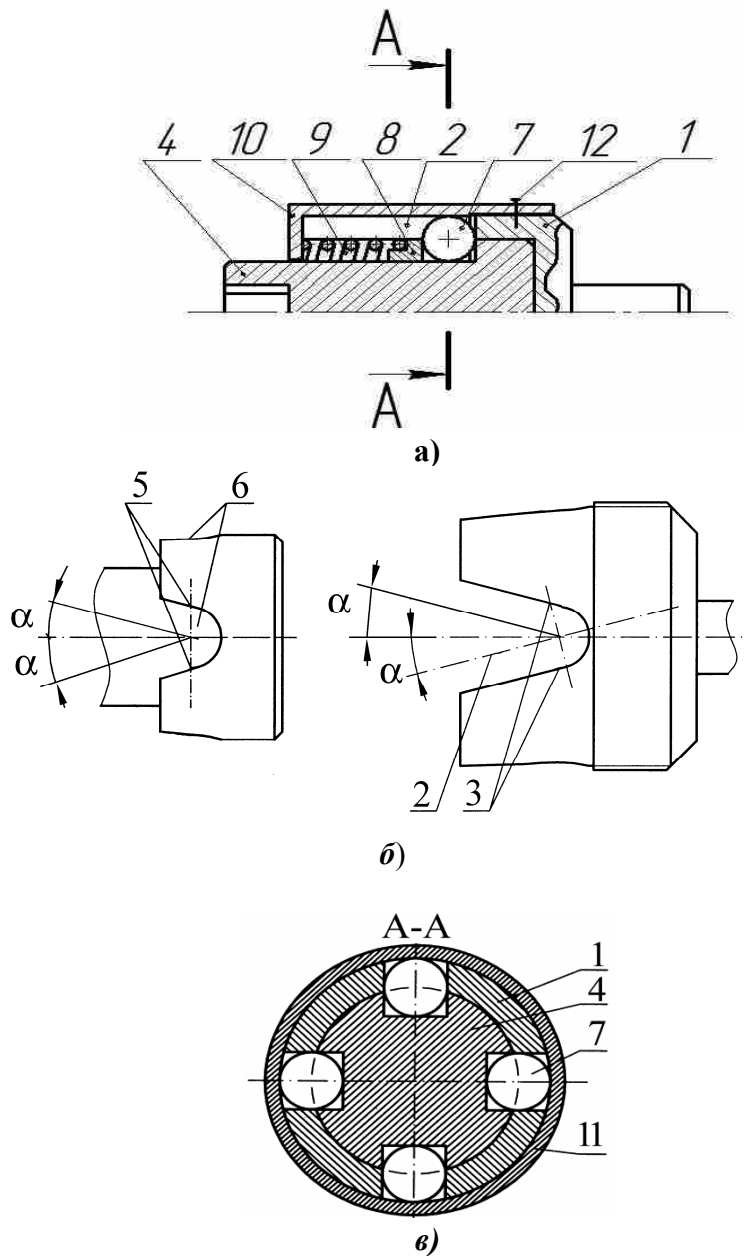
Принципова конструкція кулькової муфти: *a* – загальний вигляд; *б* – форма пазів; *в* – перетин А-А
